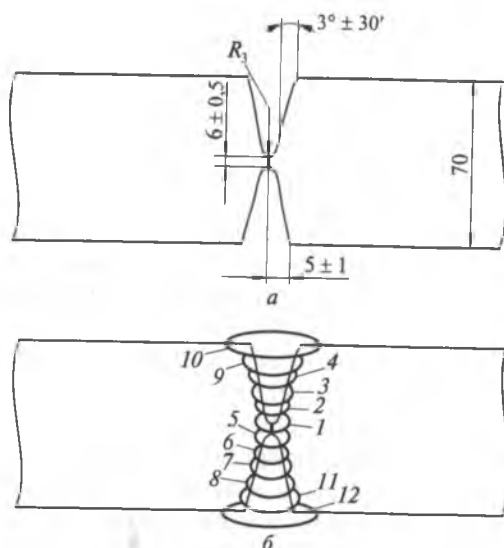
Подготовка кромок к сварке (а) и порядок наложения слоев (б)
